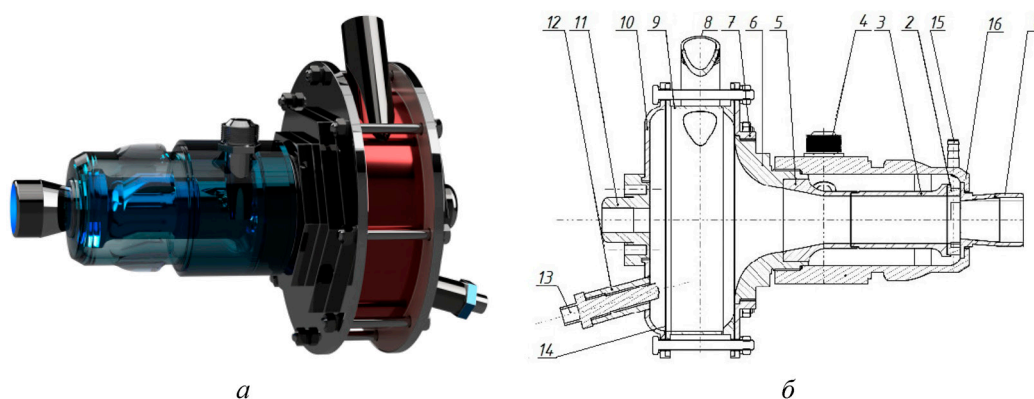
Внешний вид (а) и схема проточной части (б) вихревого противоточного горелочного модуля со ступенчатой подачей воздуха: 1 – сопло-диафрагма; 2 – закручивающее устройство; 3 – цилиндрическая вихревая камера; 4 – штуцер подачи первичного воздуха; 5 – коническая вихревая камера; 6 – переход; 7 – фланец; 8 – штуцер подачи вторичного воздуха; 9 – тороидальная вихревая камера; 10 – торцевая стенка; 11 – форсунка подачи основного топлива; 12 – штуцер свечи зажигания; 13 – свеча зажигания; 14 – прокладка; 15 – штуцер подачи дополнительного топлива; 16 – корпус охлаждающей рубашки
